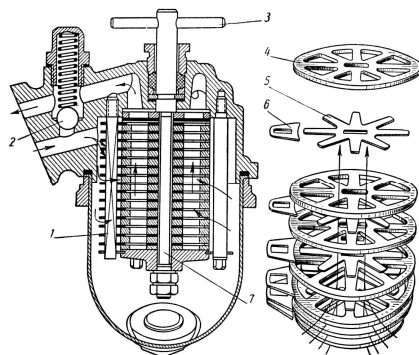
Пластинчато-щелевой фильтр: 1 – квадратный стержень; 2 – перепускной клапан; 3 – рукоятка; 4 – фильтрующая пластина; 5 – промежуточная пластина; 6 – скребок; 7 – центральный стержень.
